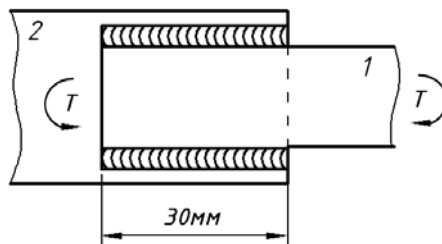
Сварное соединение полосы с косынкой
